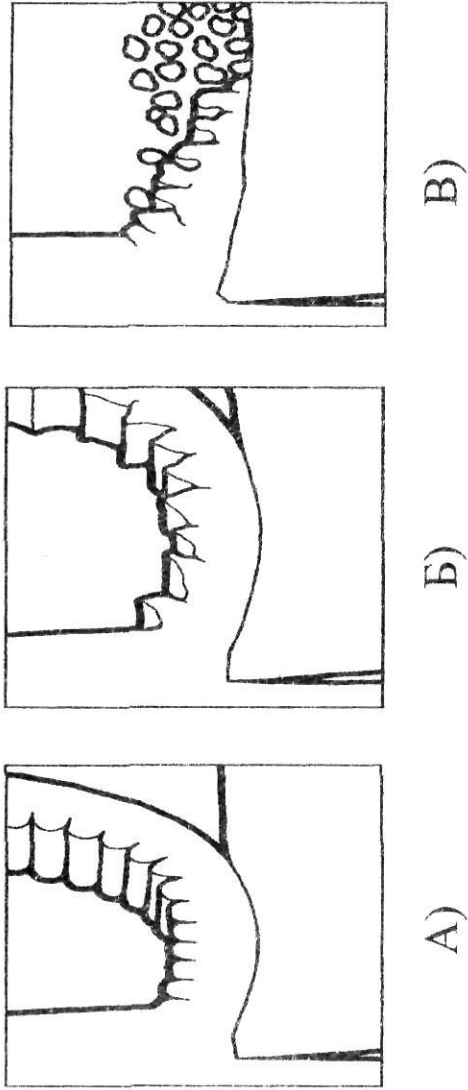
Схема формирования различных типов стружки в зоне режущего клина
